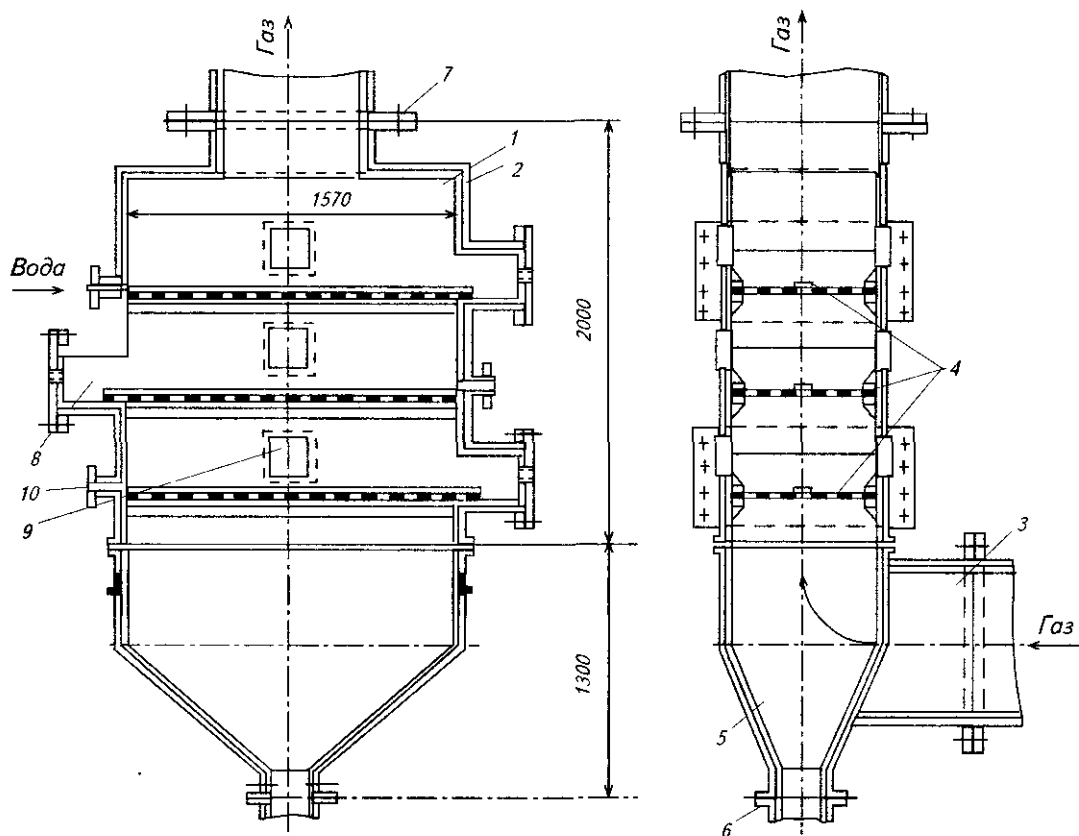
Барботажный газопромыватель для охлаждения и очистки газовой смеси
